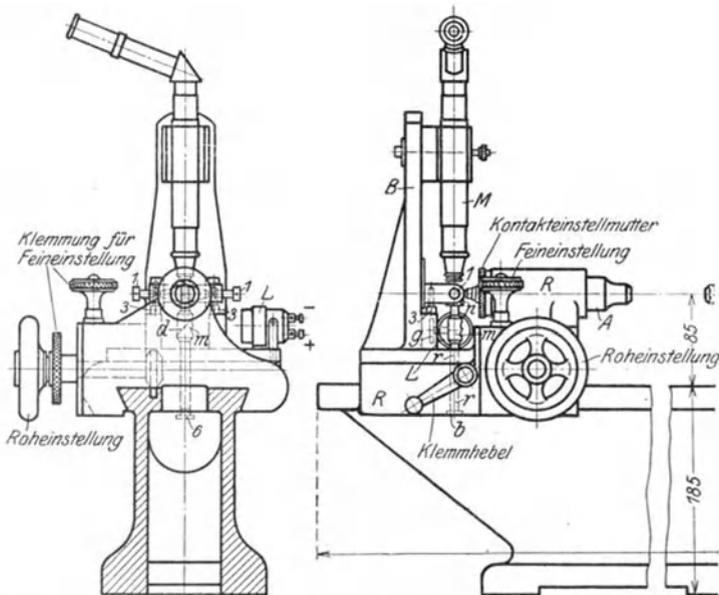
und 9. Meßmaschine mit optischem Fühlhebel. Sautter & Meßner, Aschaffenburg.
